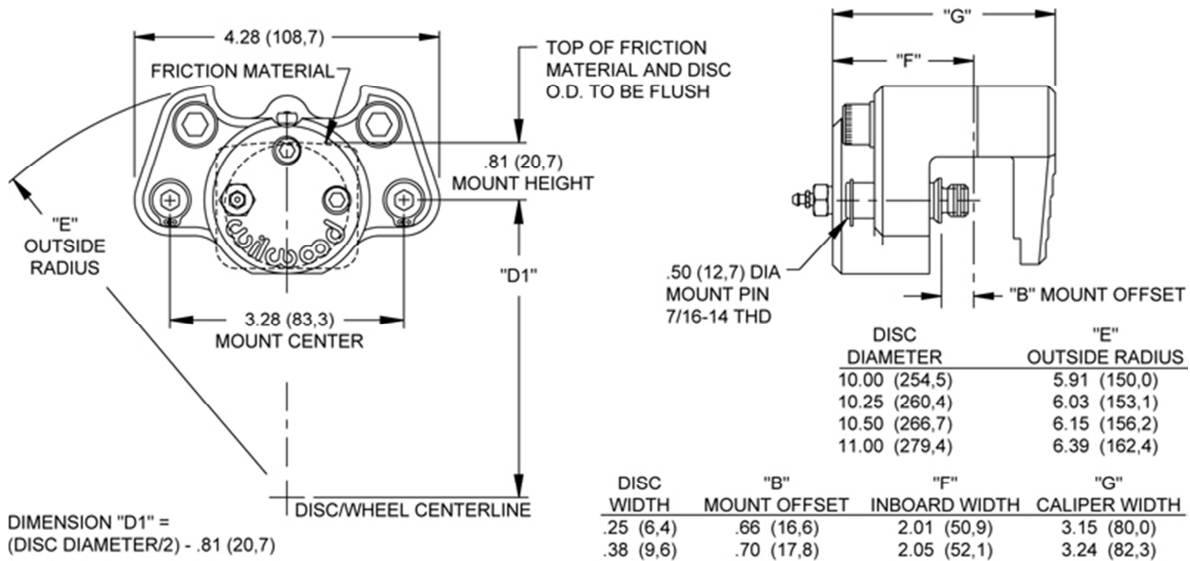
8 Dibujo técnico provisto por el fabricante de las mordazas.
